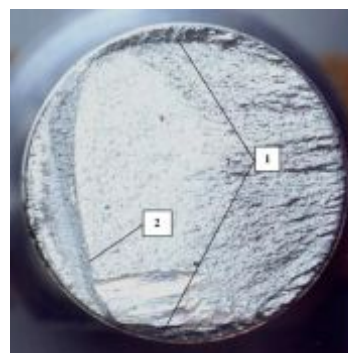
Излом образца из сплава Д16Т с медленно растущей усталостной трещиной:
